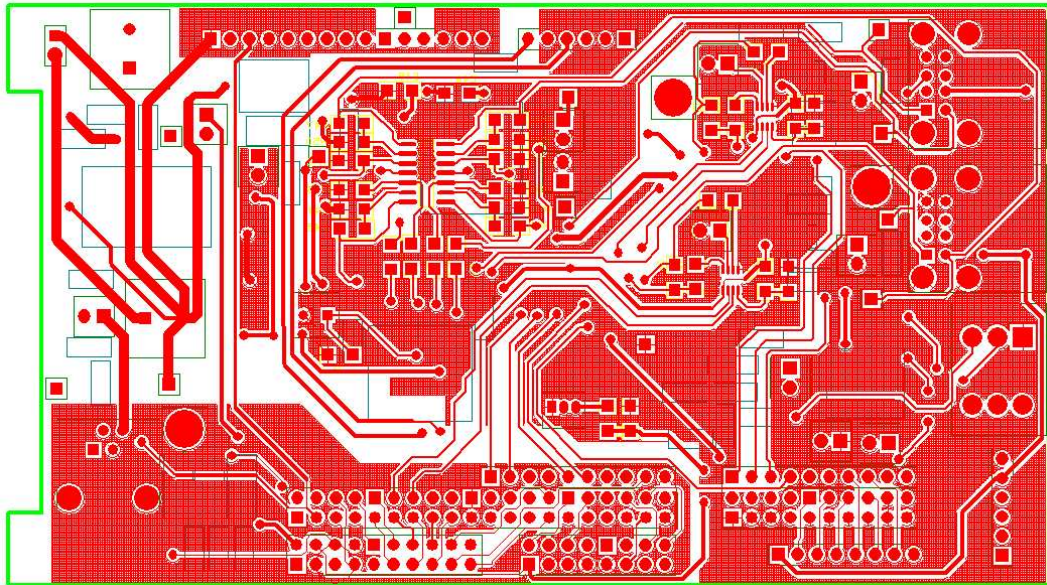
Layout do PCB da *LocusBoard* - Bottom (Fonte: [17]).
